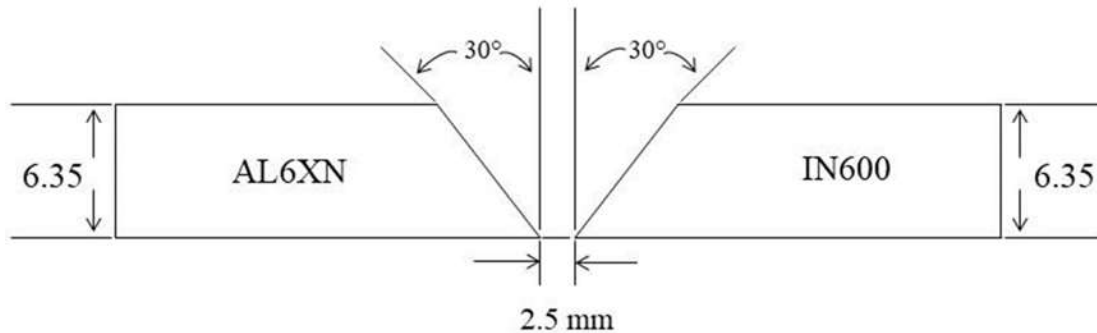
Diseño y dimensiones (mm) de la junta soldada disímil.
